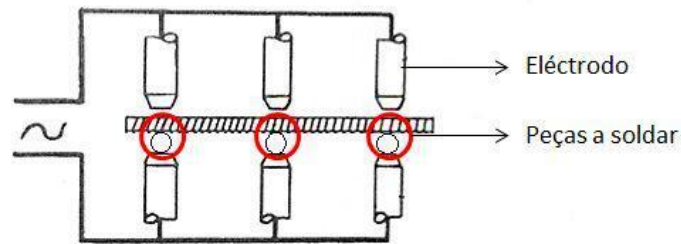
Esquema de uma máquina de soldadura por pontos múltiplos. Adaptado de [9].
